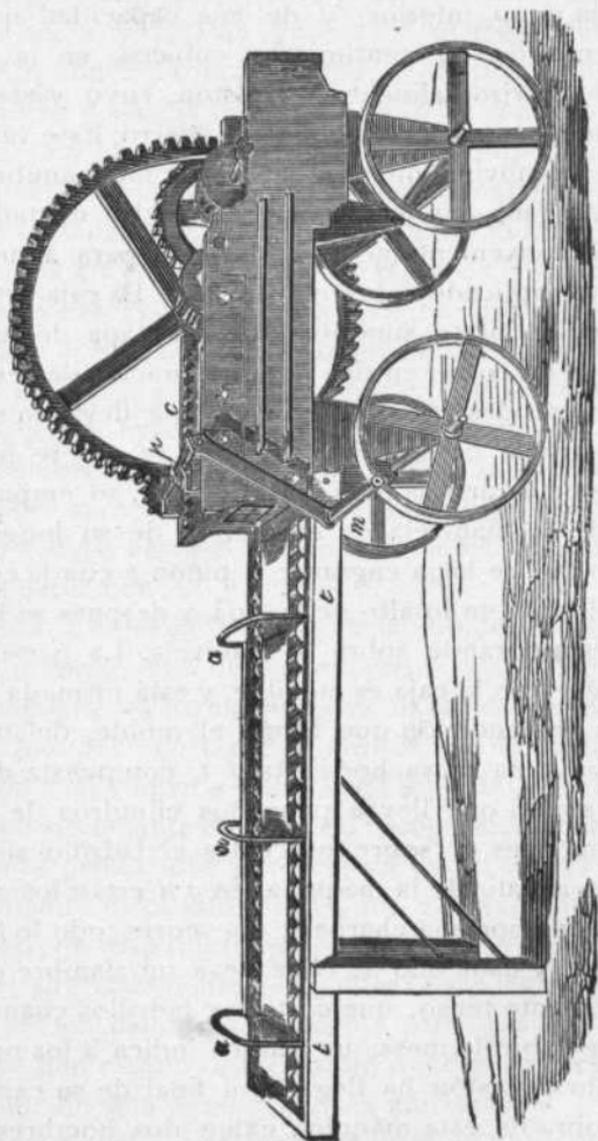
Máquina de Doyte para moldear ladrillos con hileras, movida a brazo
